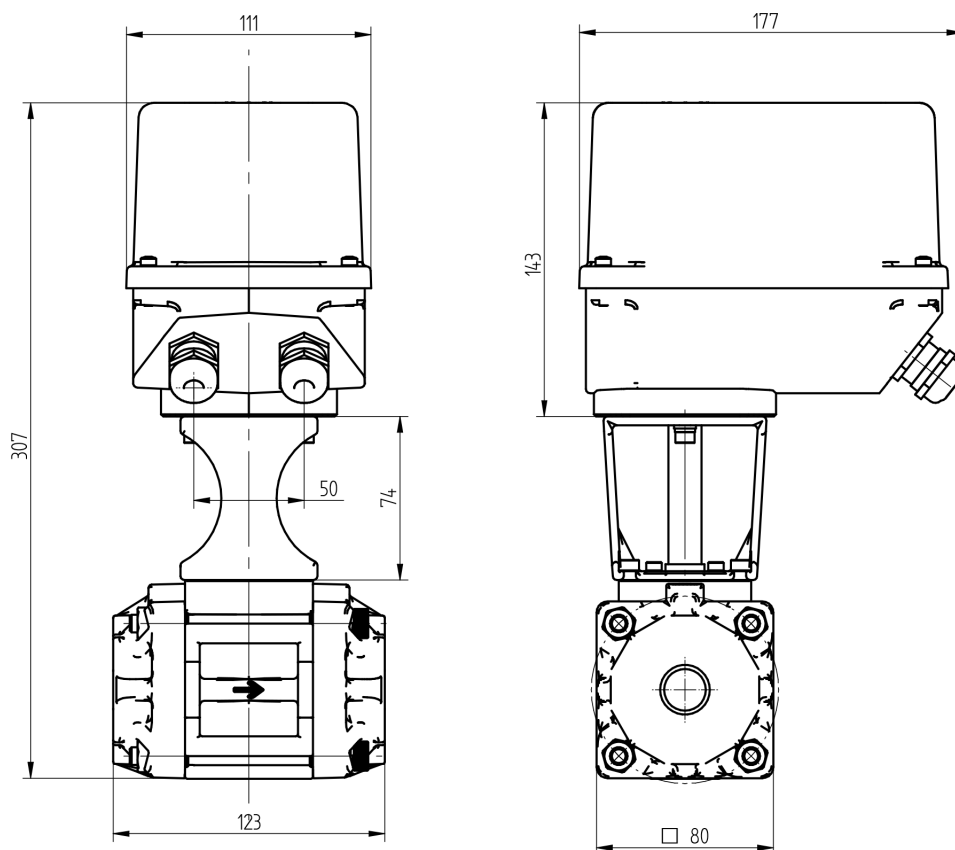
Maßzeichnung Gasstellglied Typ SVL – 668M2400 montiert auf Stellantrieb (Maße in mm)
